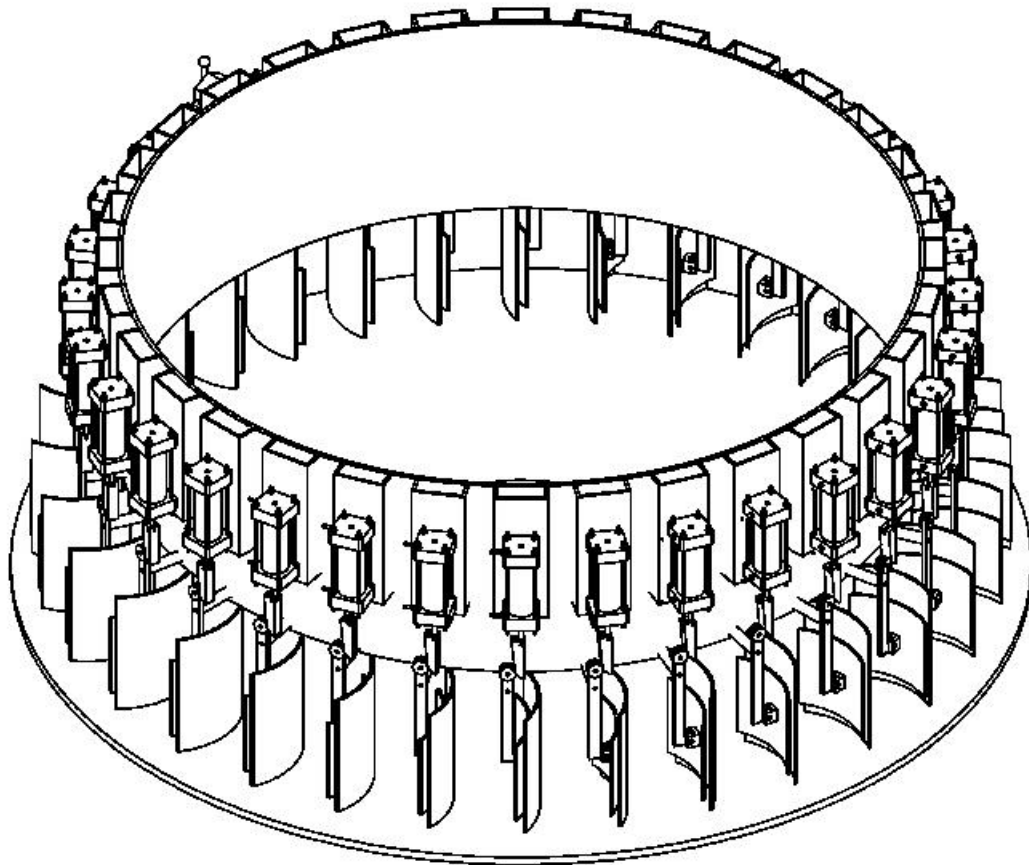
Сборка-сварка лопатки и диска
